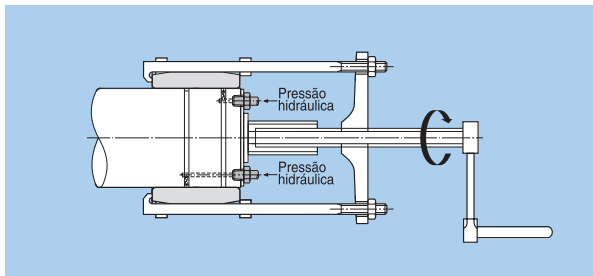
Desmontagem utilizando óleo com alta pressão (hidráulico)
